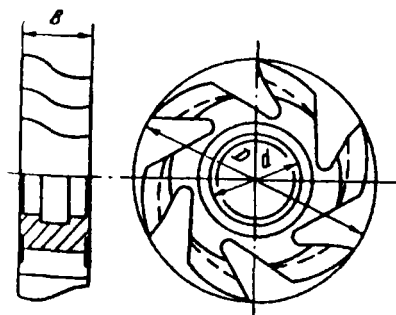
Пример фрезы для обработки строительных деталей (прорезная для фрезерования шпатов и проушин в брусках створок и коробок)
